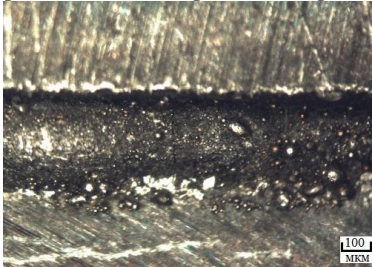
Внешний вид поверхности сварного шва пластин ЧВГ 35 и ЧВГ 30, при номинальном расходе аргона, увеличение $\times 75$
